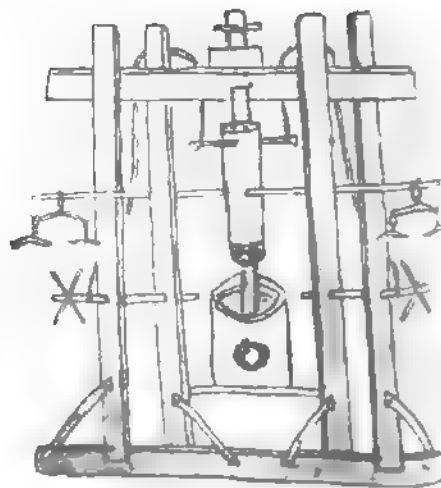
Bohrmaschine für Geschütz, durch Göpel bewegt, um 1450.
